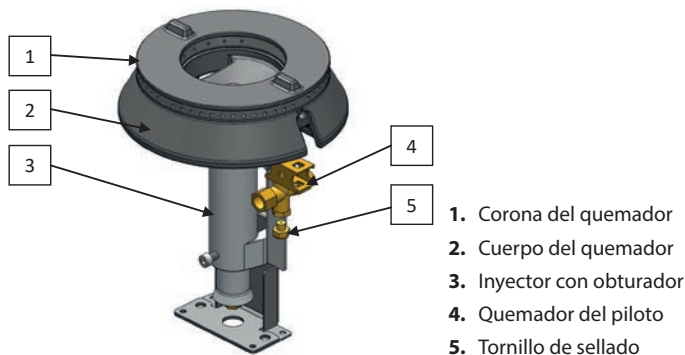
Diseño del quemador sobre el ejemplo de un quemador de 7 kW.
